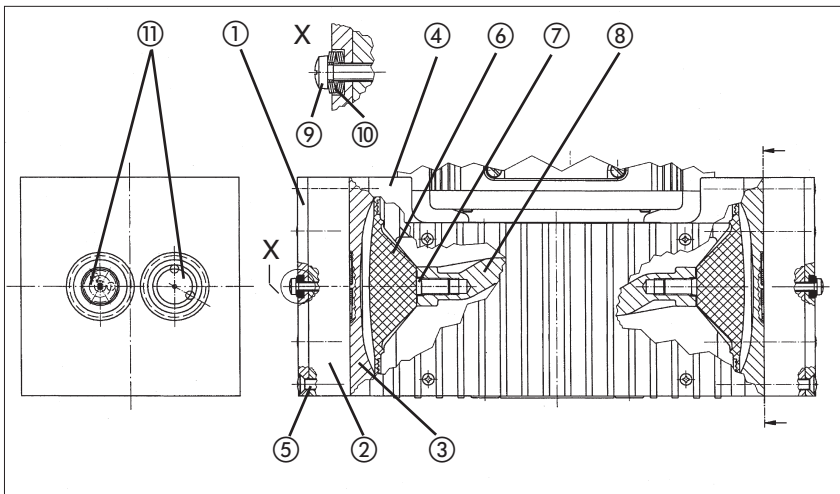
Schnitt durch die Pumpenköpfe (symbolisch)
